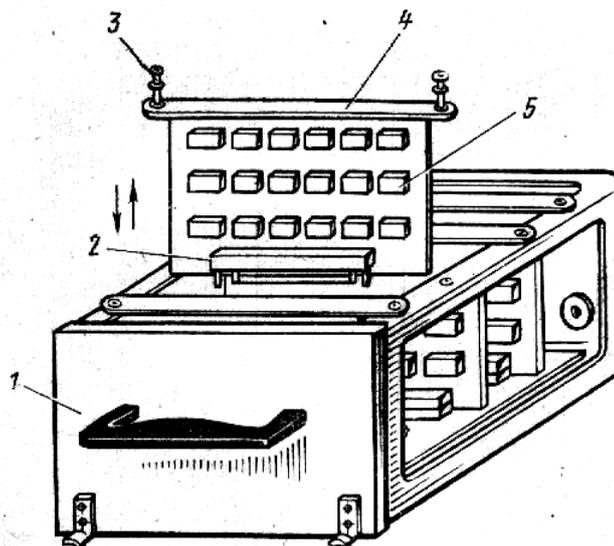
Разъемная компоновка блока МЭА: 1 - корпус;
